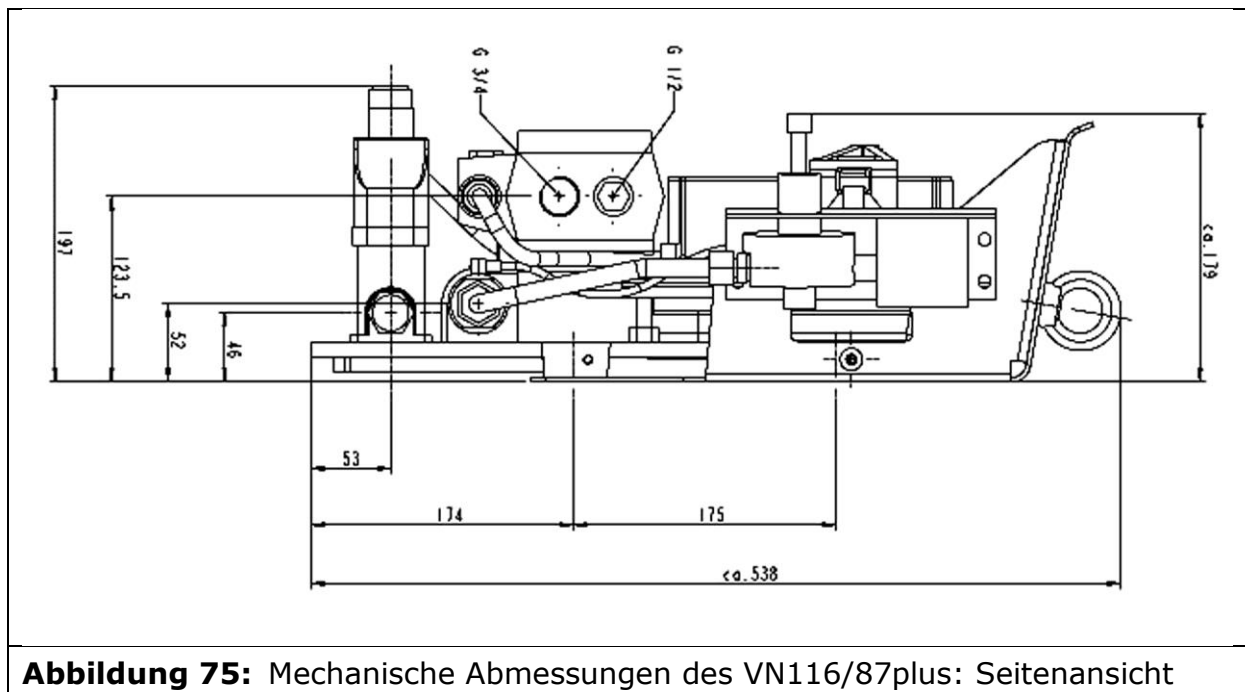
Mechanische Abmessungen des VN116/87plus: Seitenansicht
